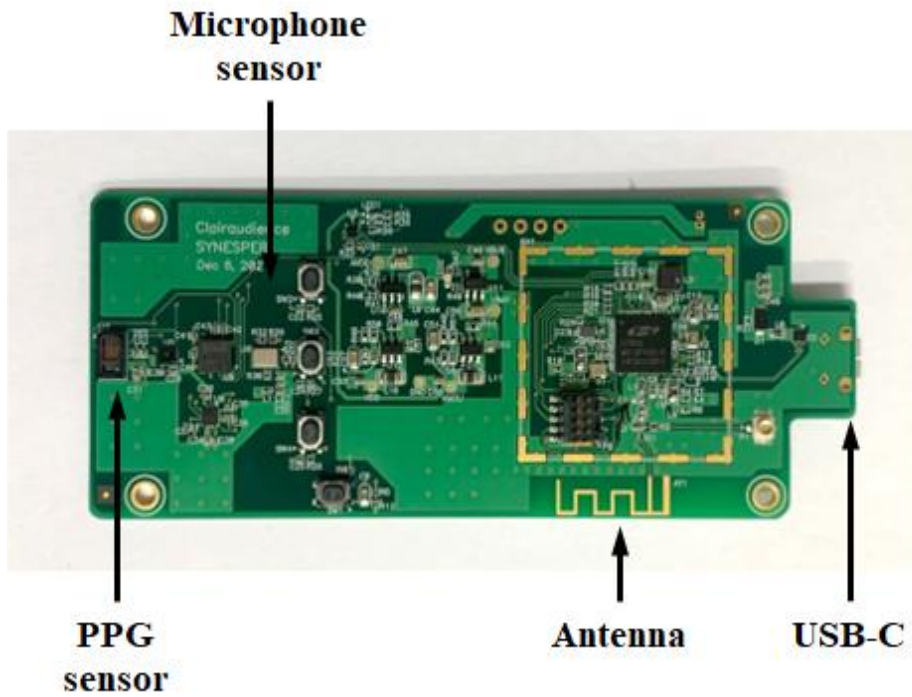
제안한 개인용 청진 시스템 PCB 제작
